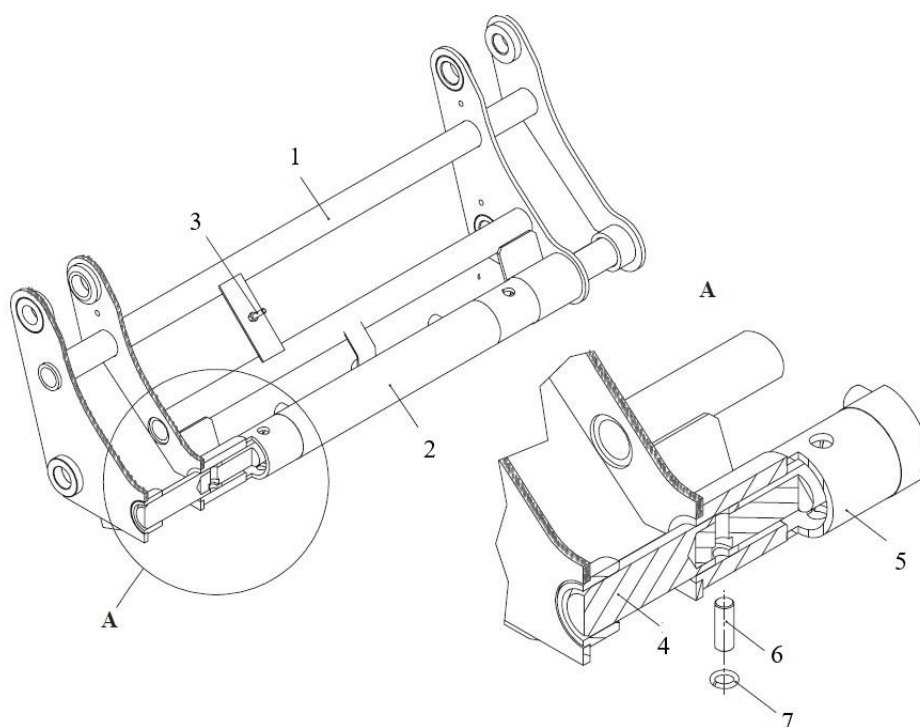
Конструкция сцепки для быстрой смены рабочих органов универсального малогабаритного погрузчика Амкодор-211
